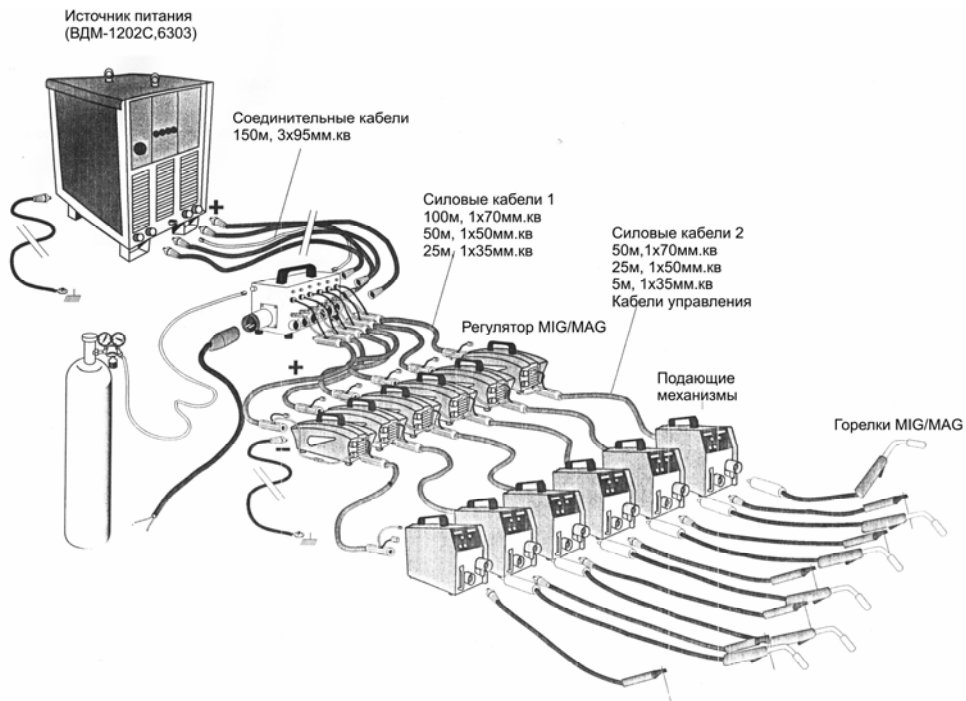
Вариант применения КСУ-400 для полуавтоматической сварки.
